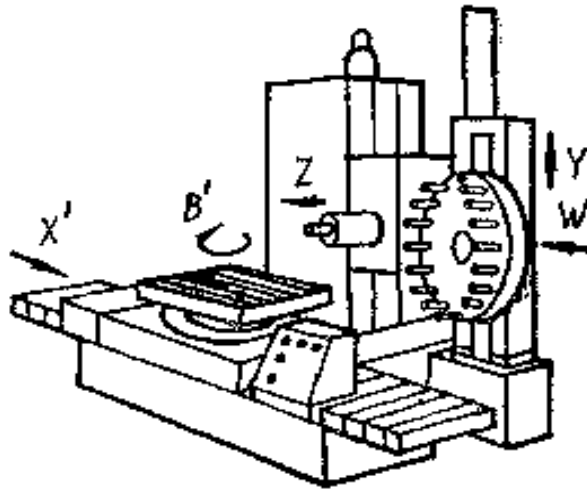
Компонувальна схема горизонтально - розточного верстата.
